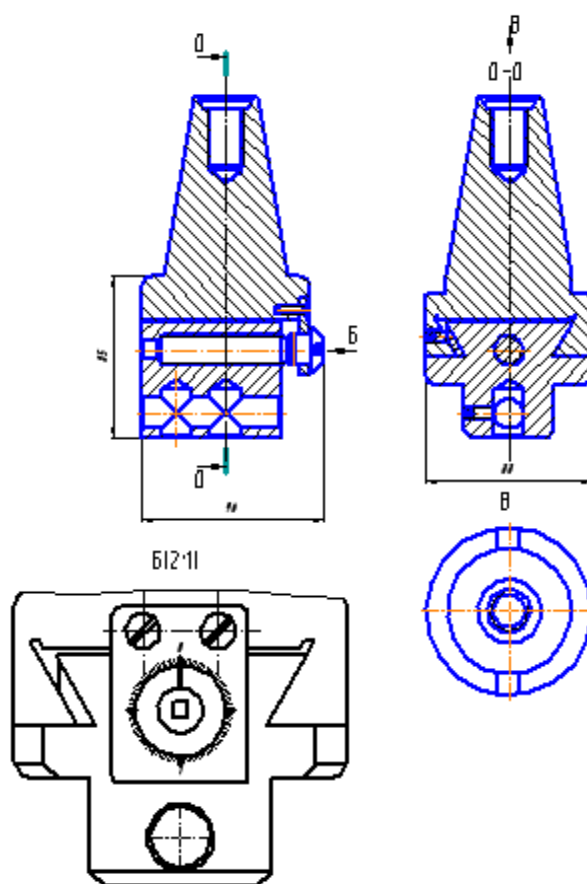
Двухмерный чертеж расточной оправки
